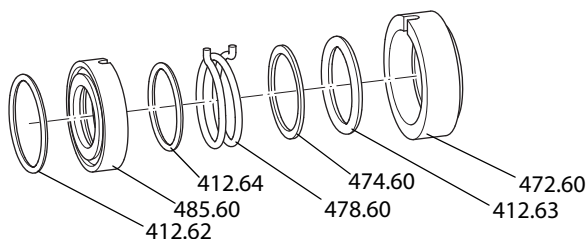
Finalizar el montaje en el árbol, aplicación B
